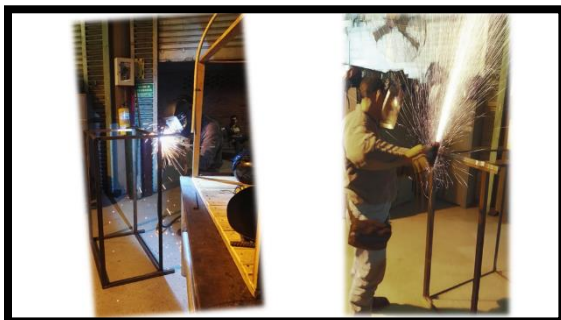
corte y soldadura de piezas; Obtenido: Semillero de investigación.
